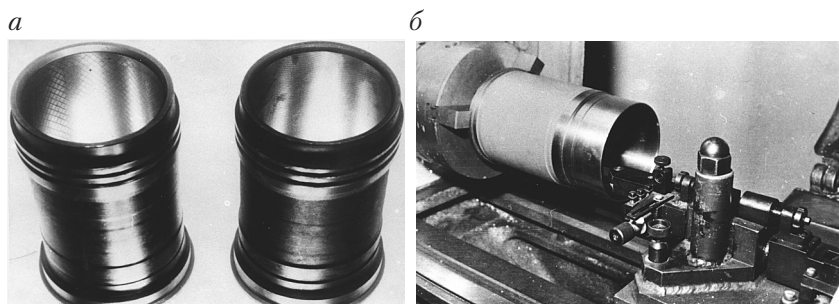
Гильзы цилиндров с РМР на зеркалах (*а*) и виброраскатывание гильзы на токарно-винторезном станке (*б*)
